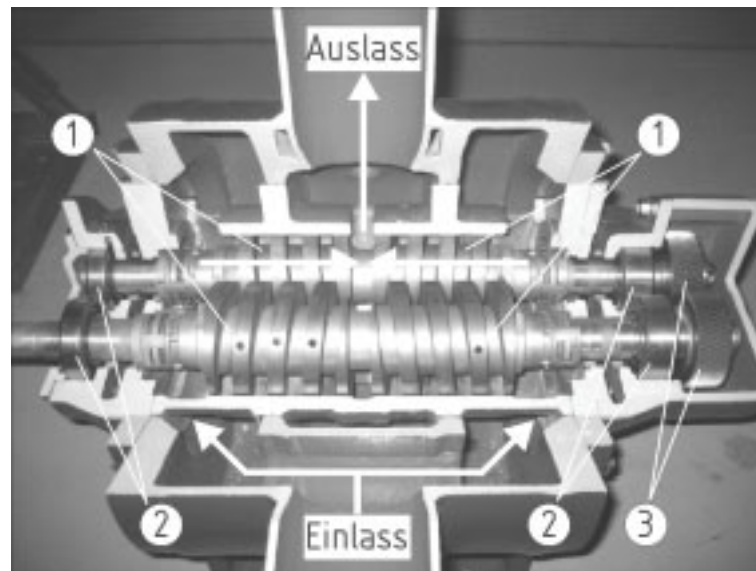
Schnitt einer doppelflutigen zweispindeligen Schraubenspindelpumpe
